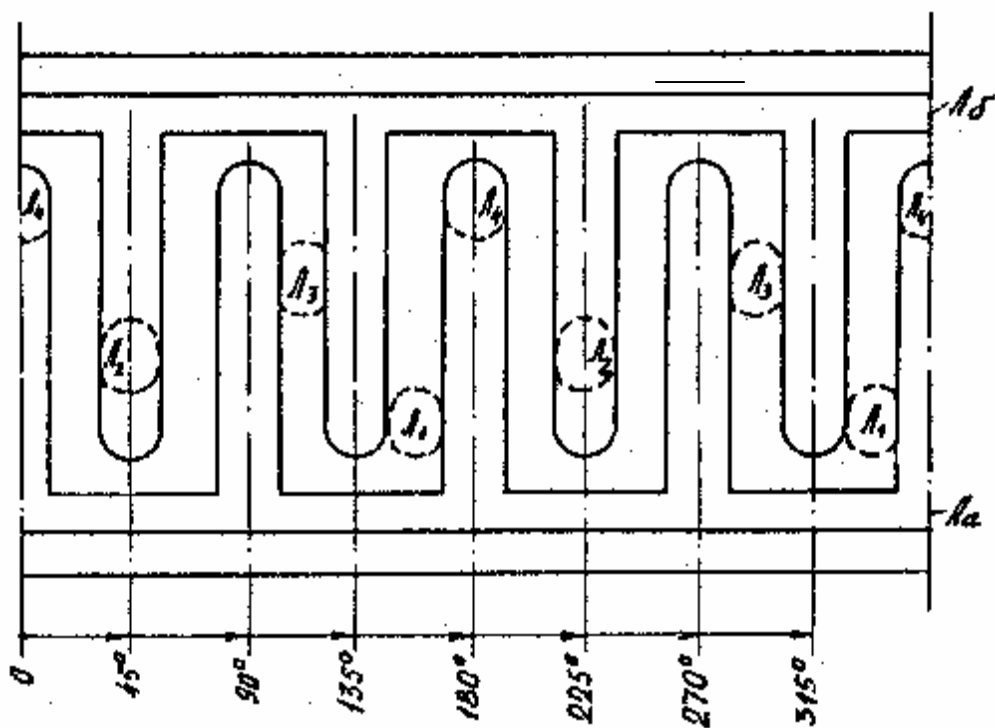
Развертка наружной поверхности золотника с обозначением размещения каналов втулки
